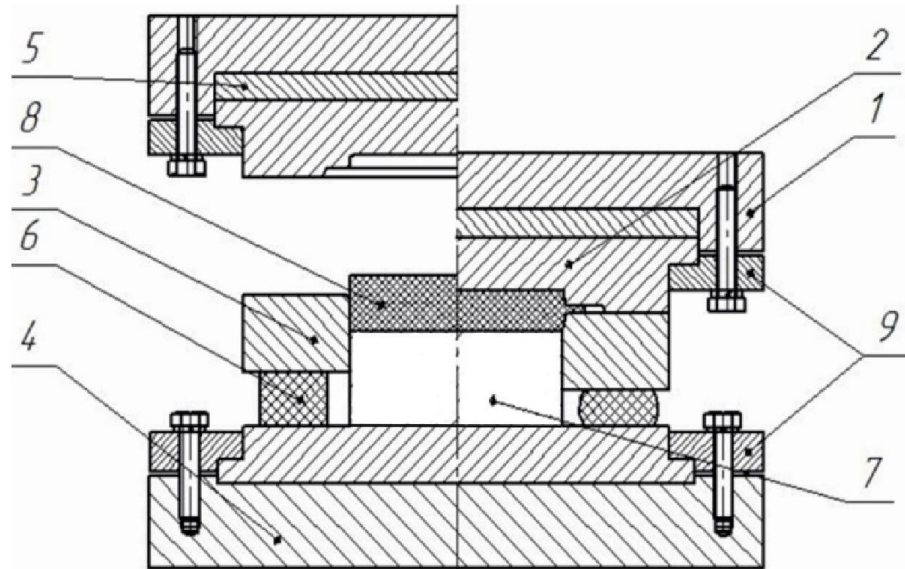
Загальний вигляд дугостаторного пресу ФА-1732
